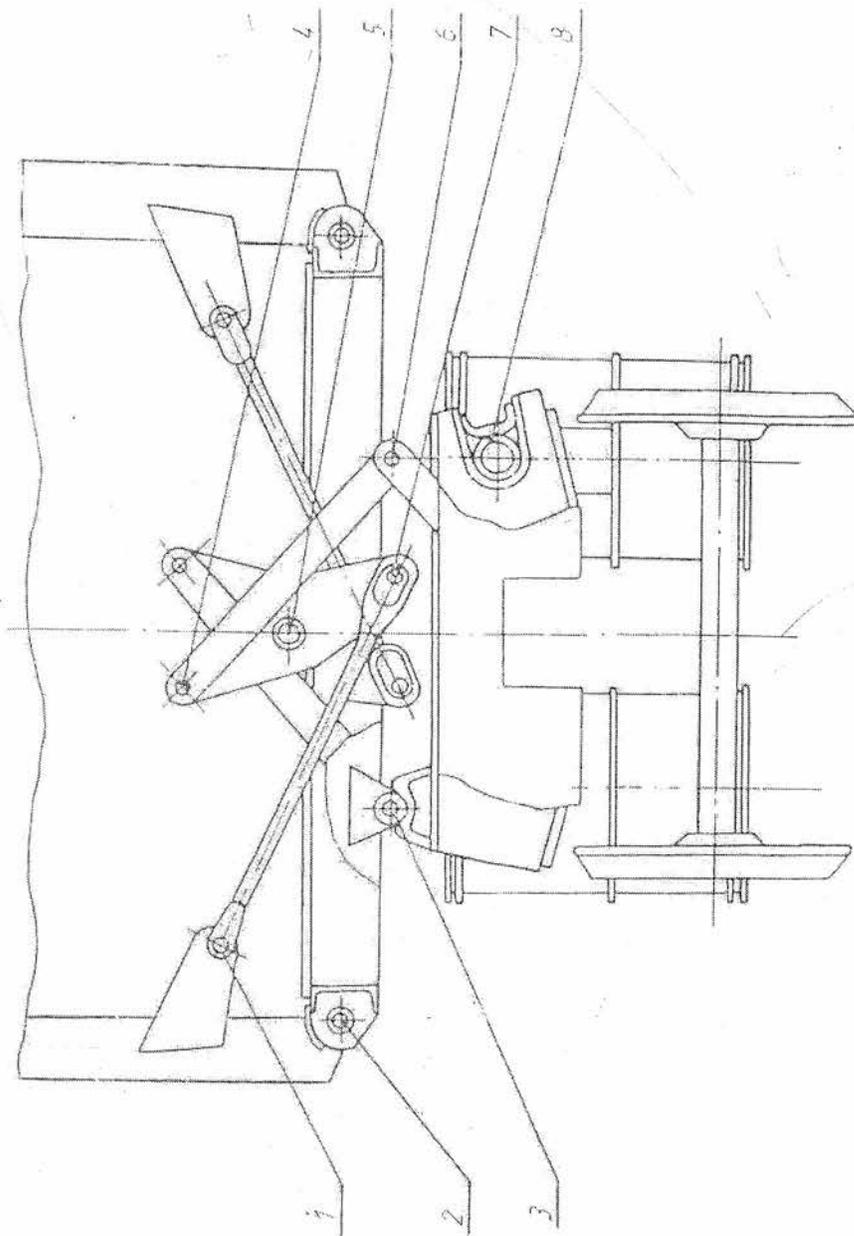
Схема смазки шарнирных соединений вагона
